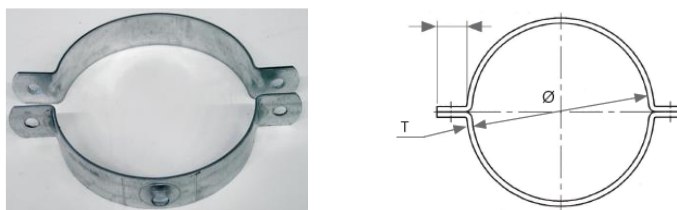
Cinta de fixação KVDA (QFS Oil Mist & Cutting Fluid)
